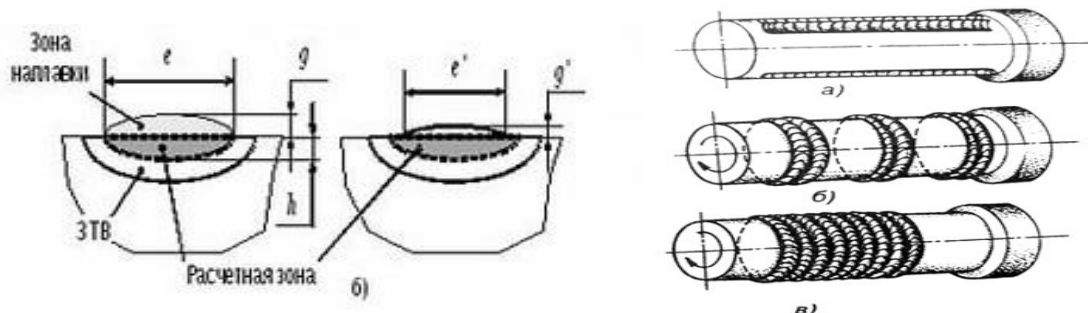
Схемы наплавки плоских и криволинейных поверхностей
